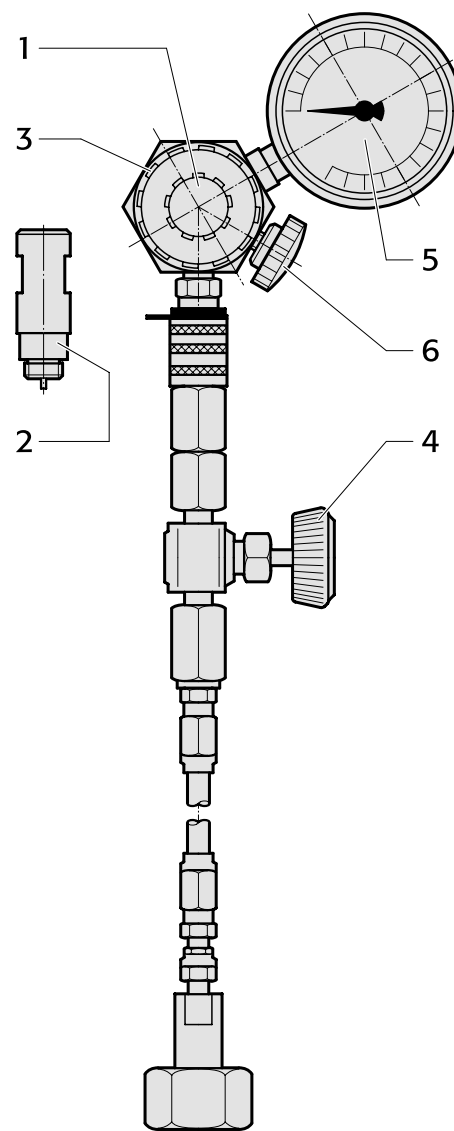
Dispositivo de llenado y control y manguera de llenado
